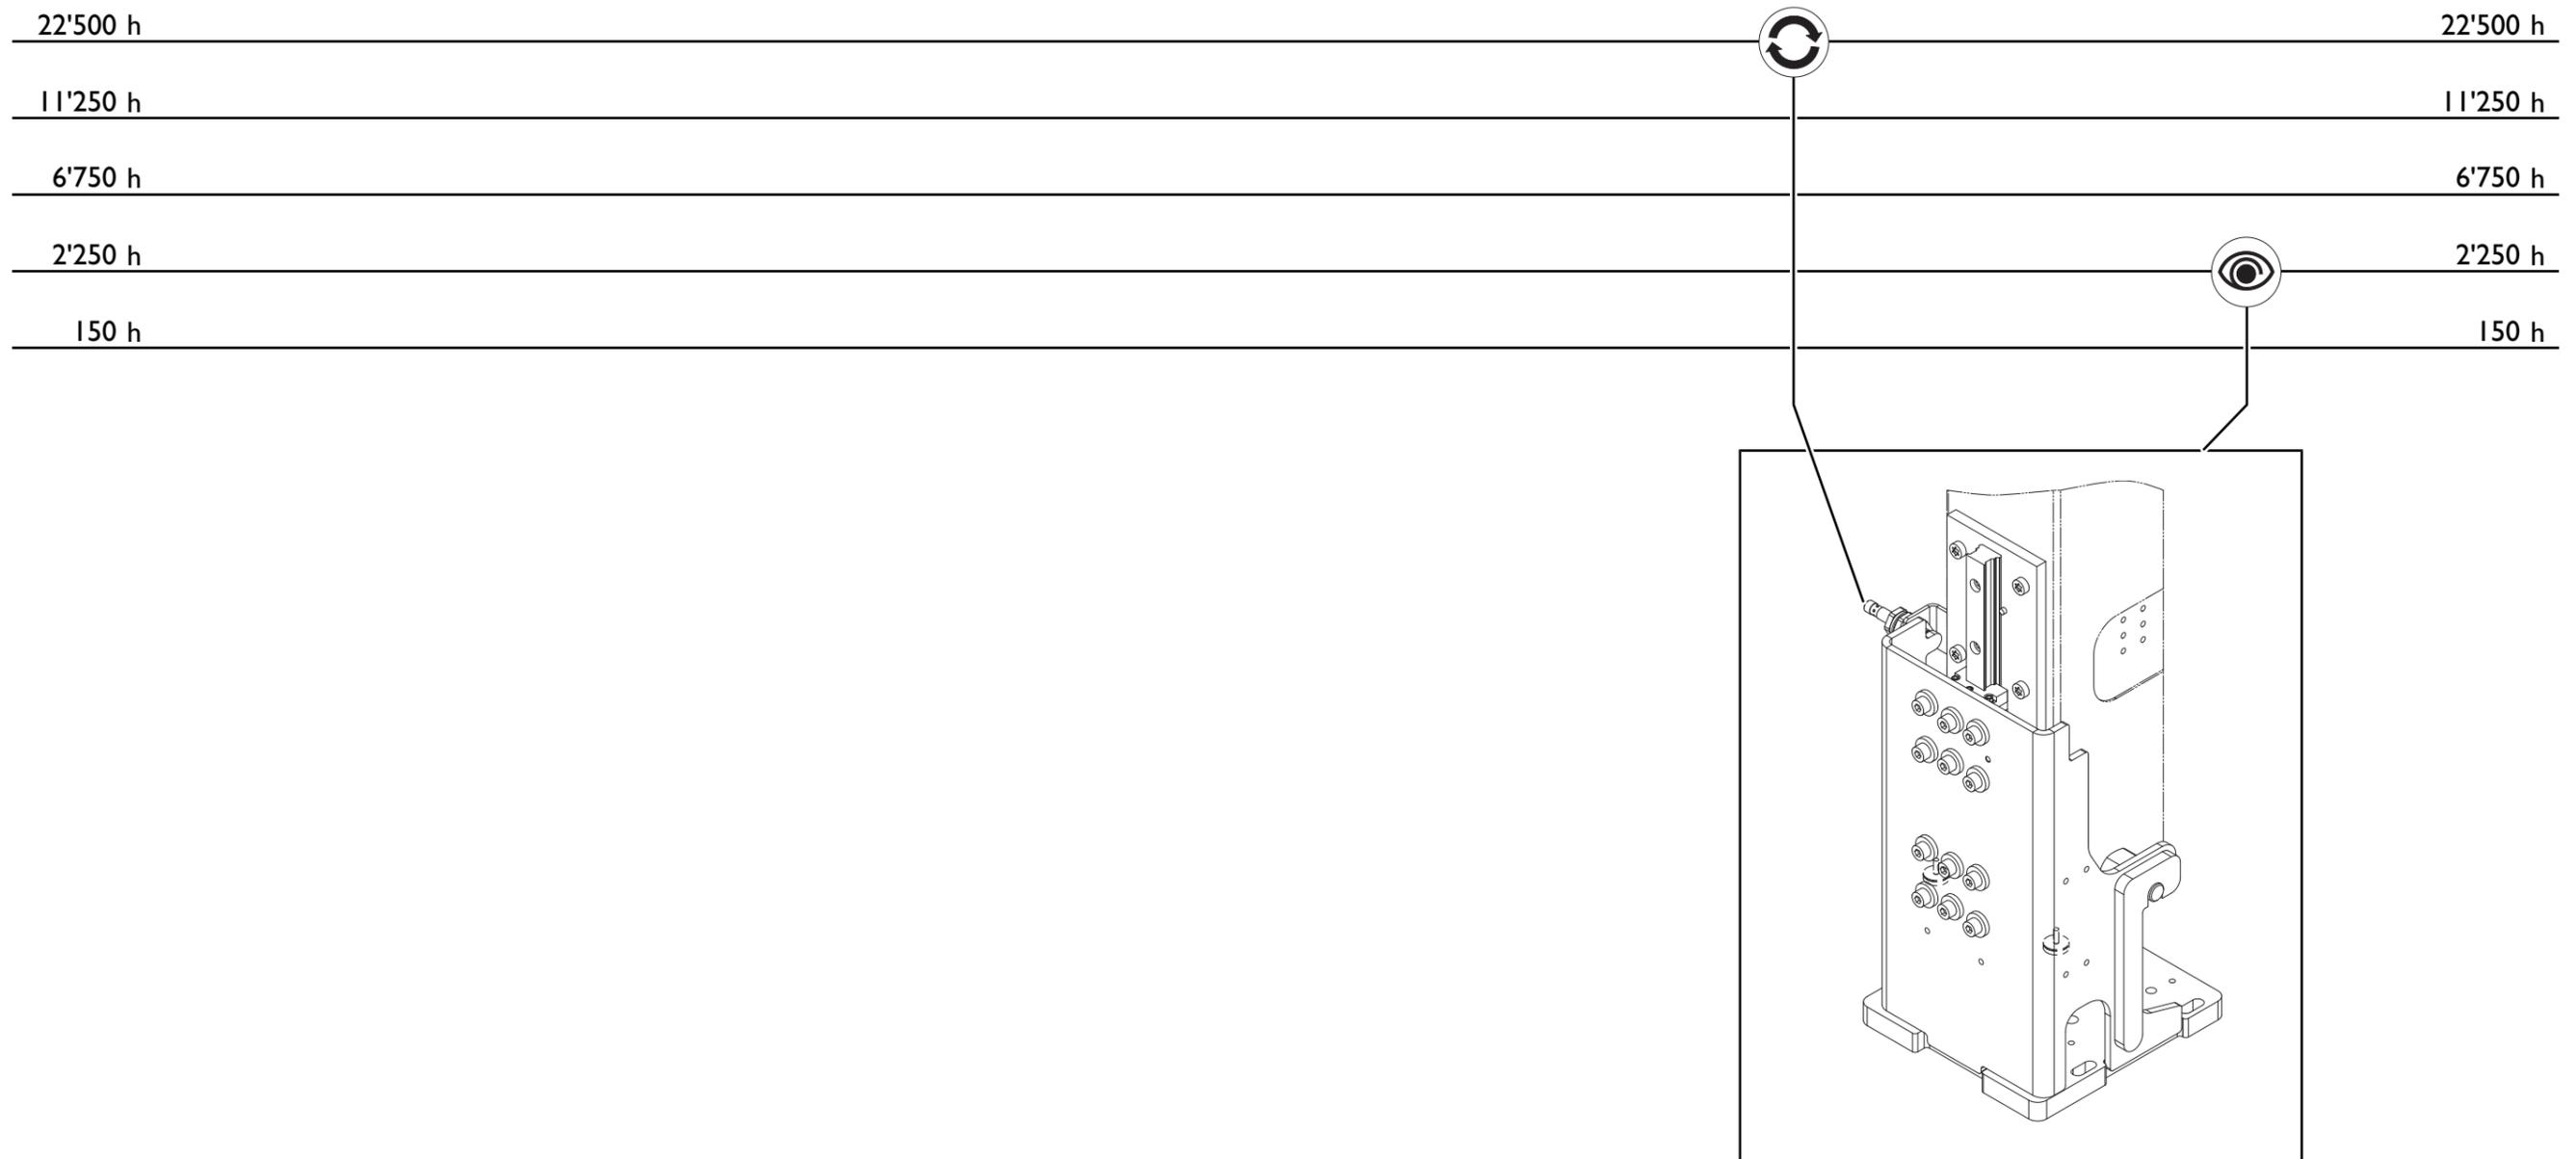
Plan de mantenimiento protección contra choques eje Z
